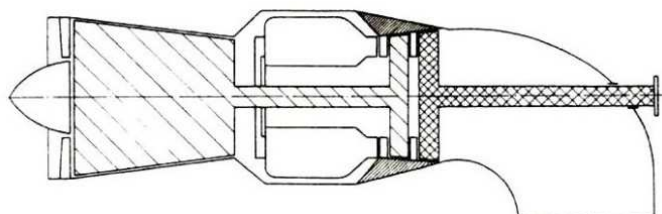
Turbodmychadlový, třírotorový, dvouproudový motor [1]
